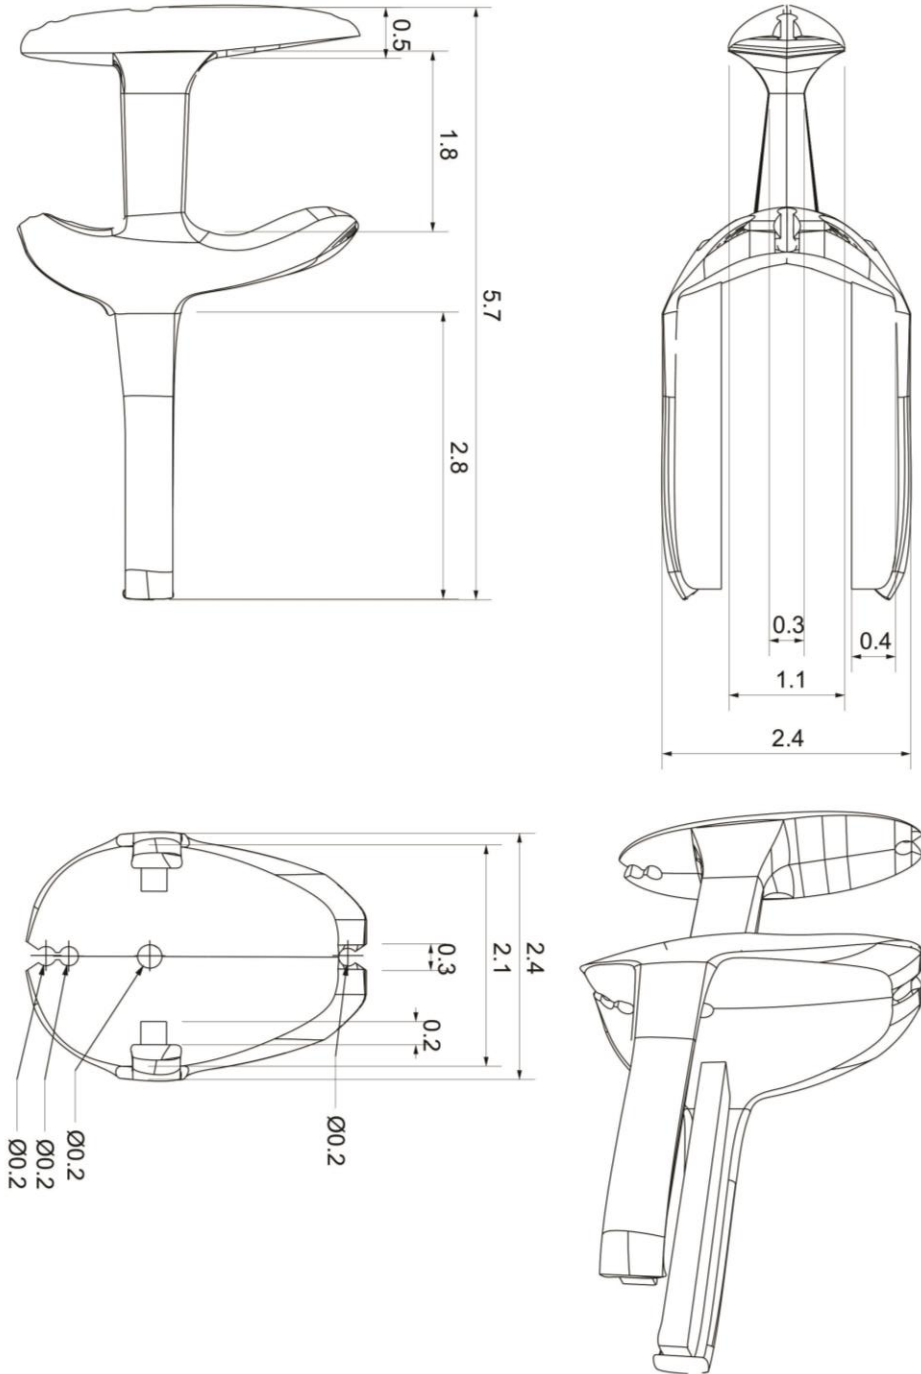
Planos pieza # 2 (Dimensiones en cm)
